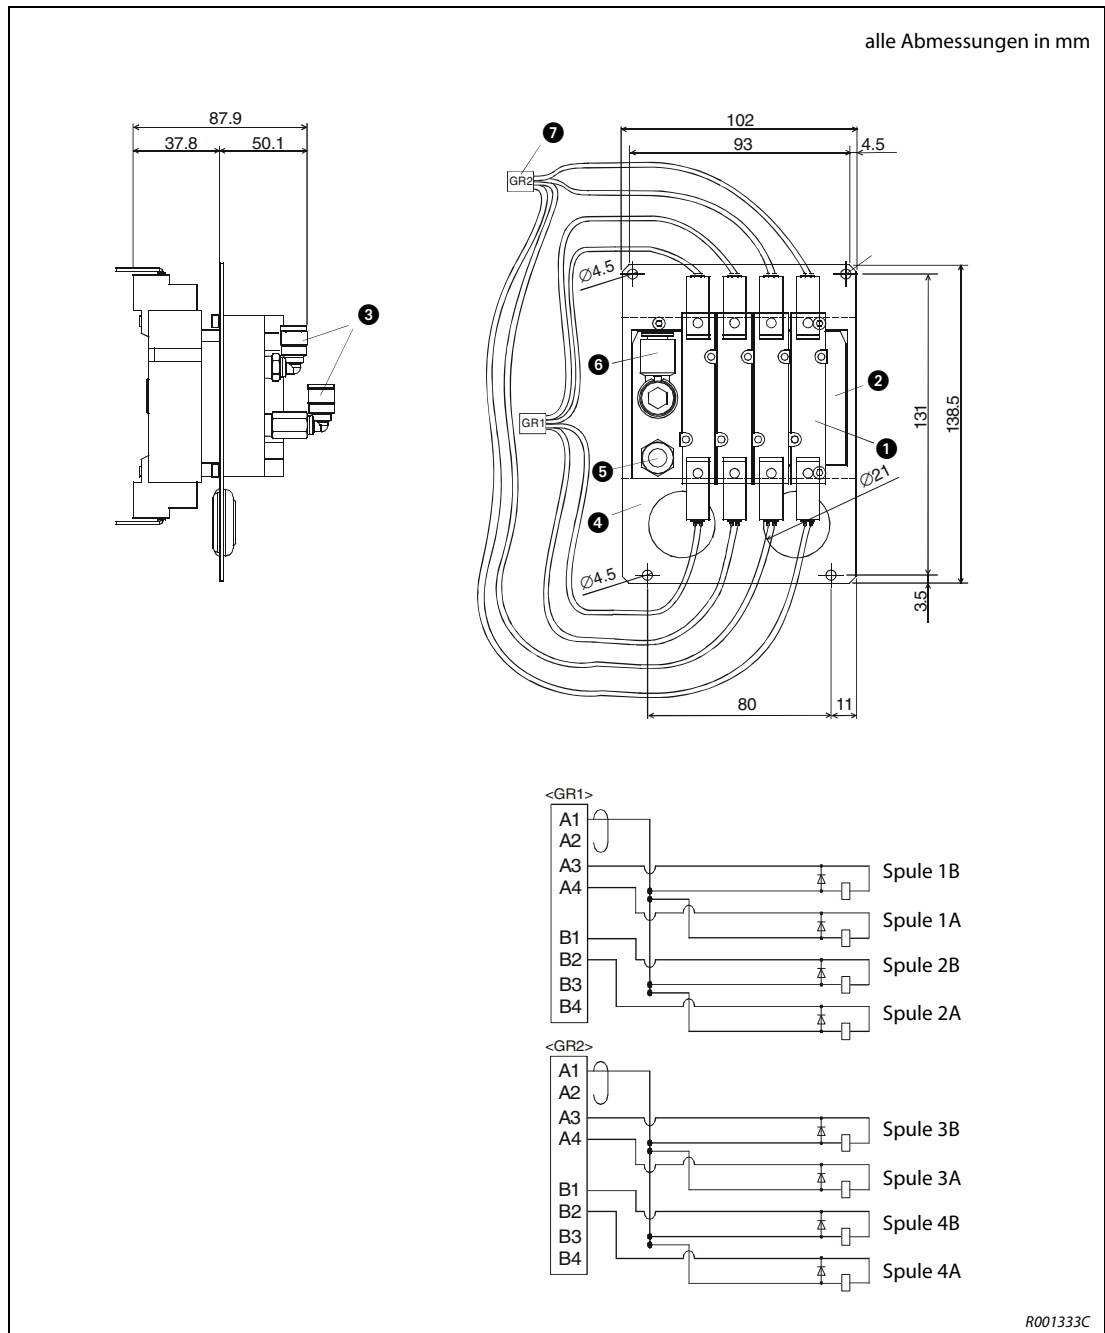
Abmessungen der Ventilbox (RH-6SDH)
